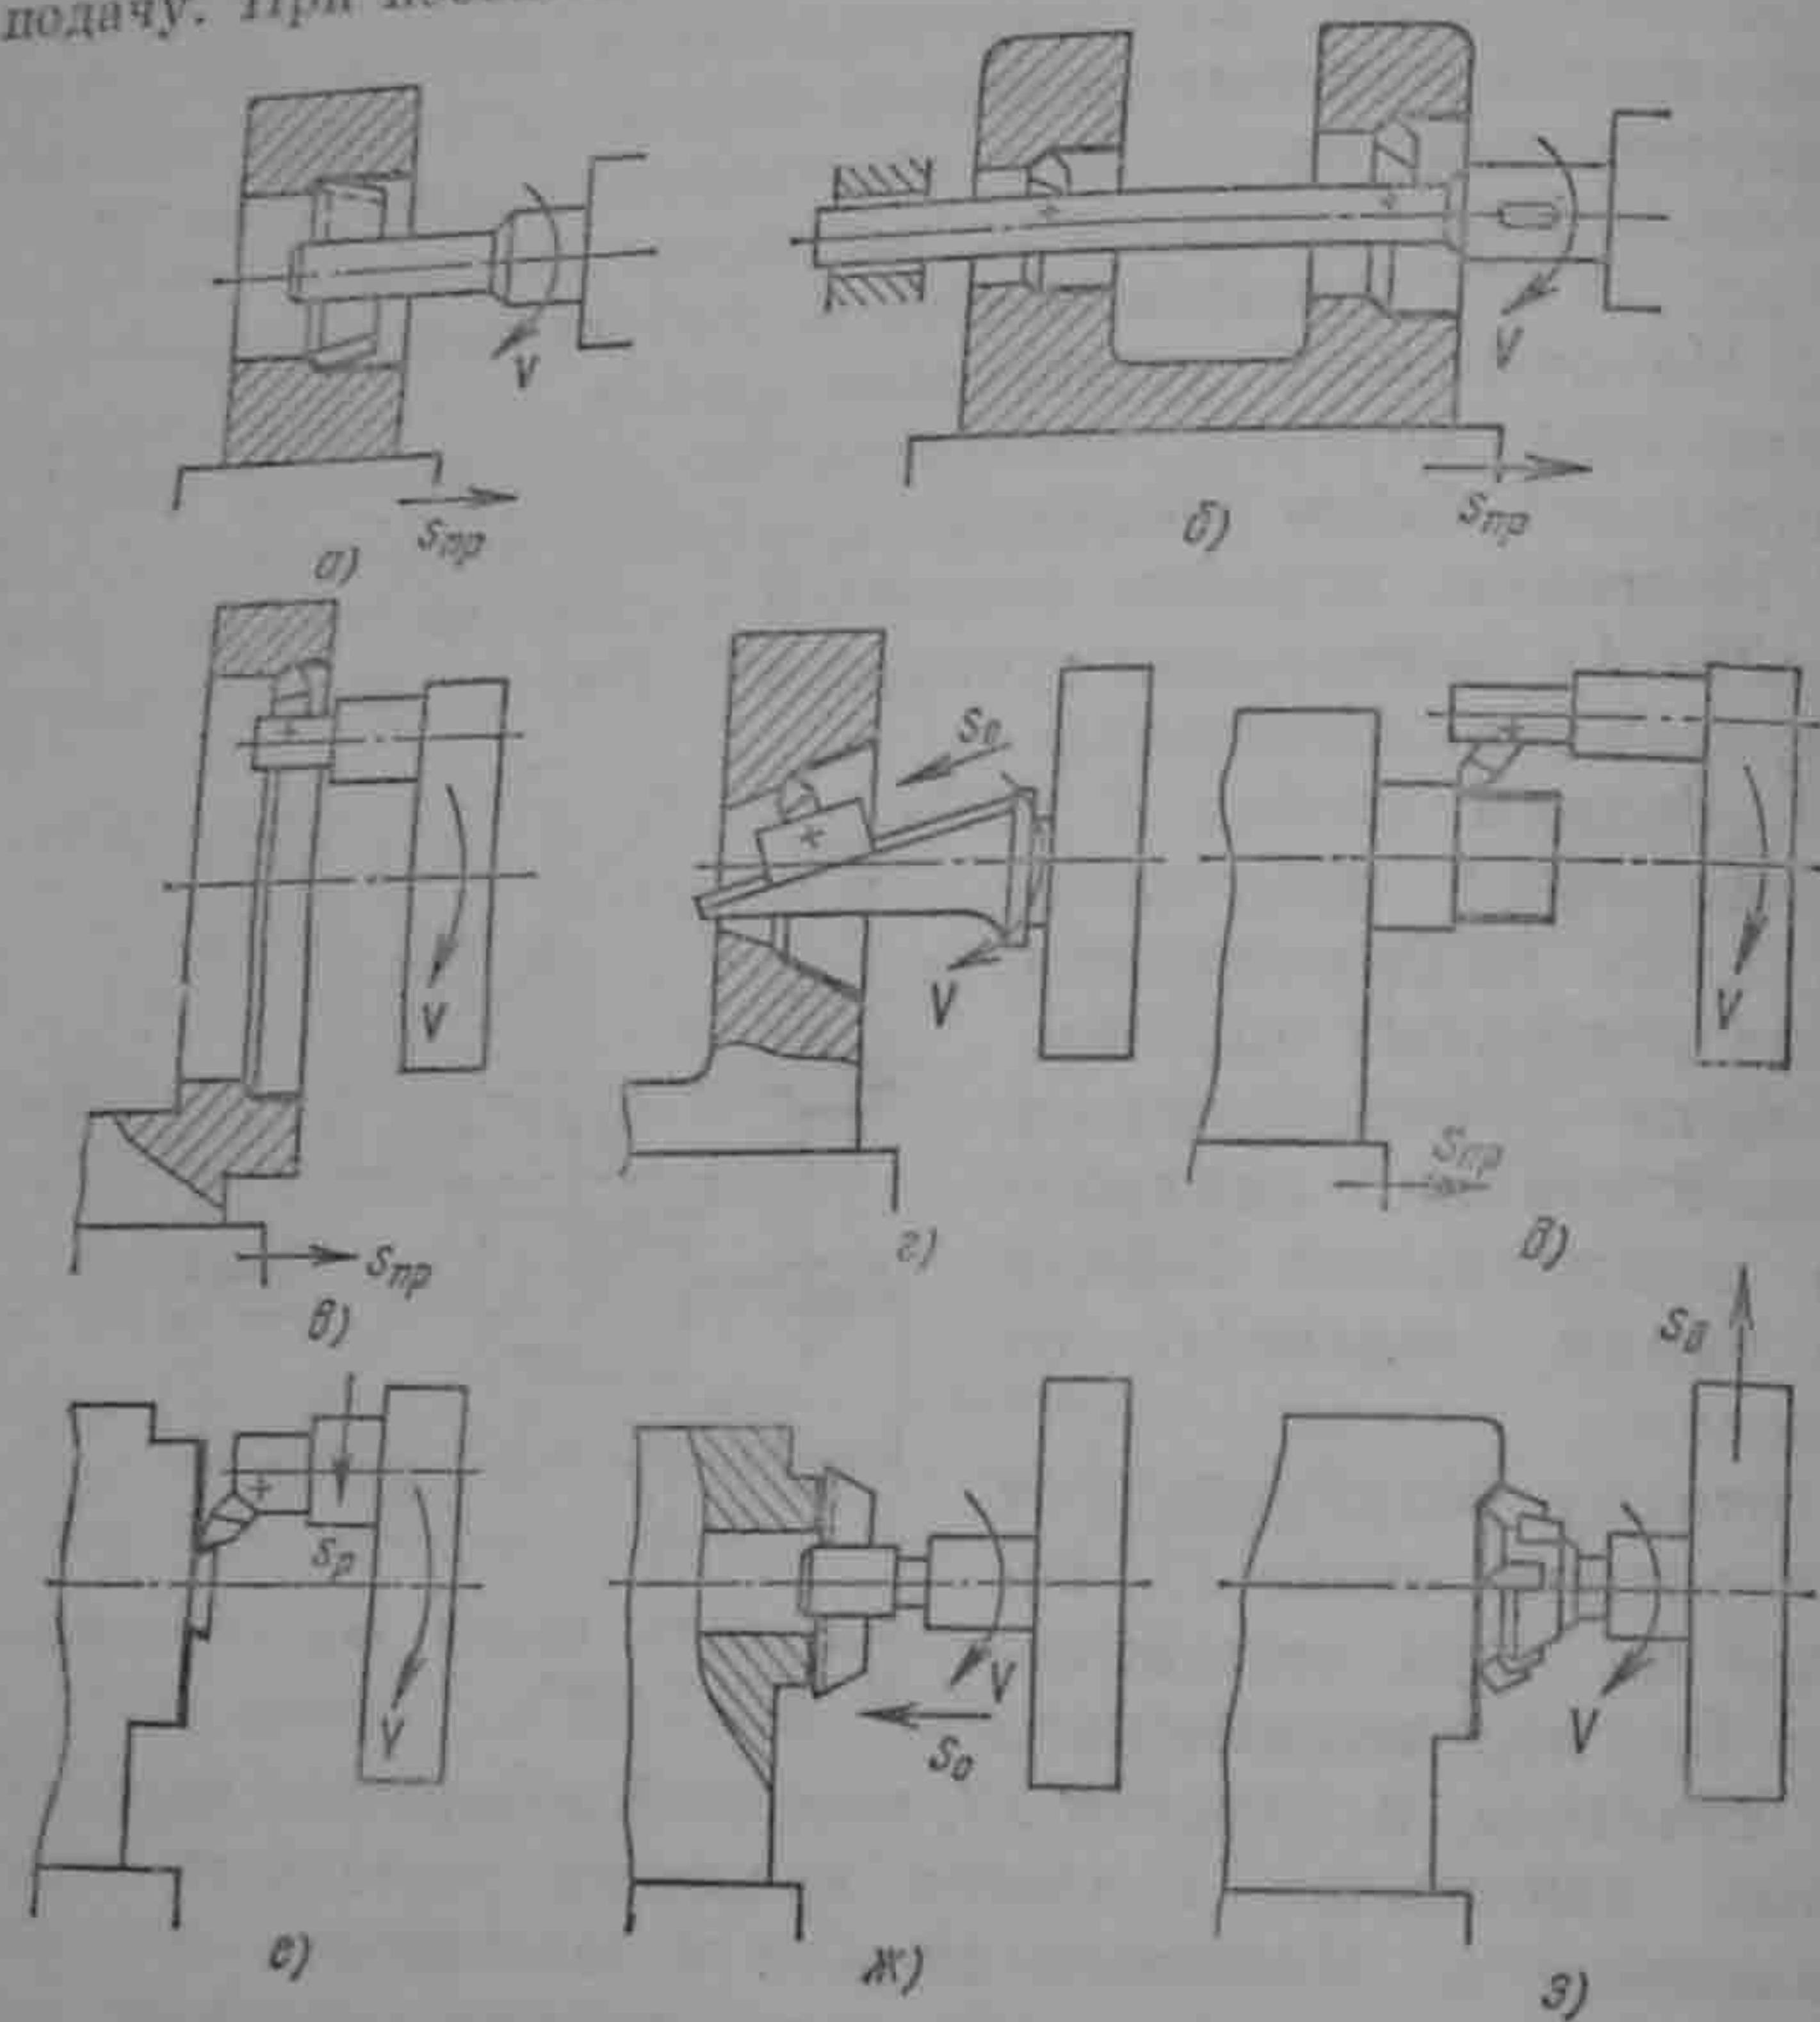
Схемы обработки поверхностей заготовок на горизонтально-расточных станках
